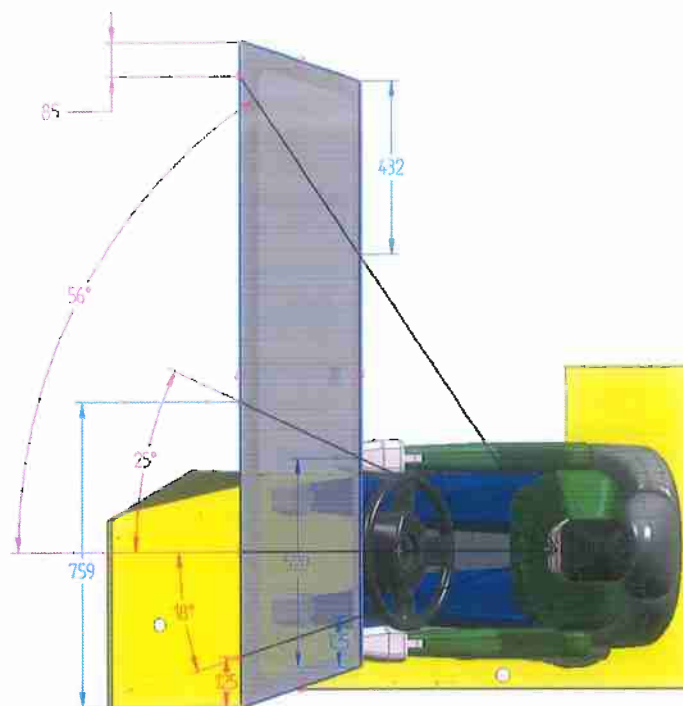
Projeções dos ângulos horizontais no veículo (unidades em mm)
